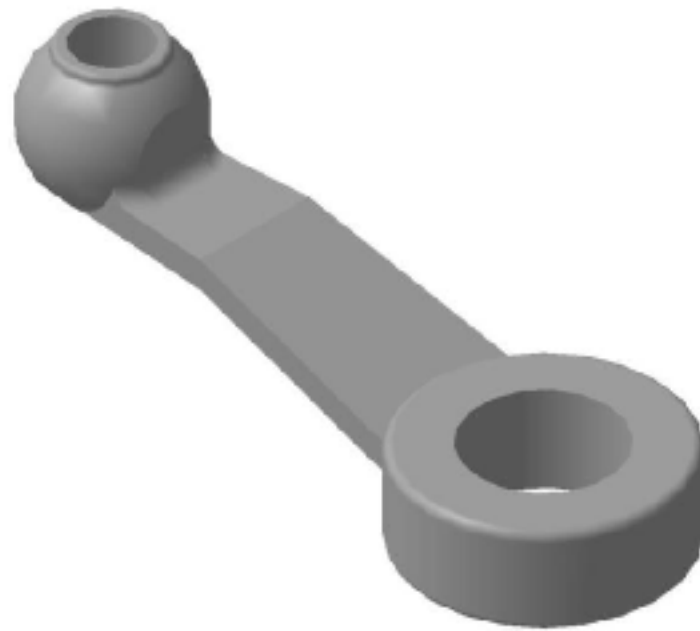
3D-модель заготовки виготовленої литтям за виплавними моделями
